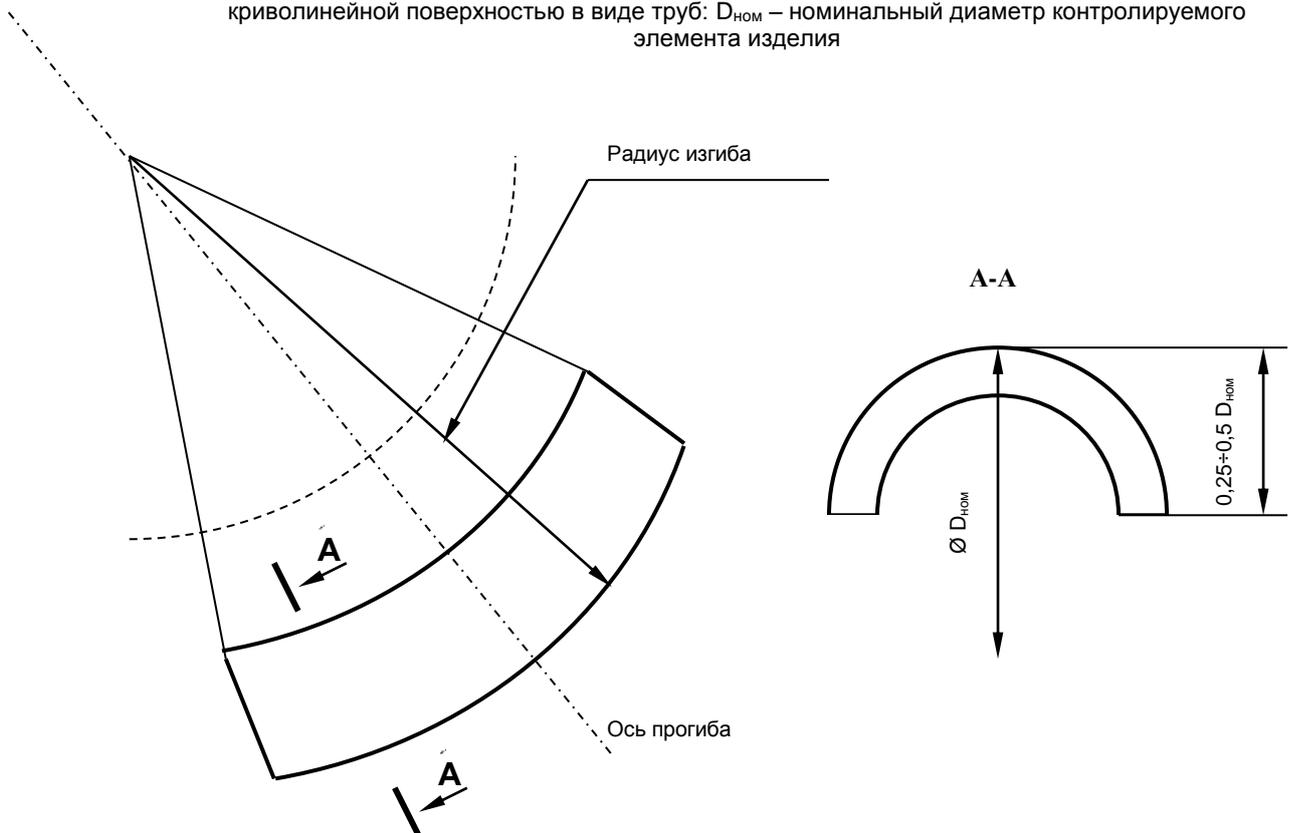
КО для настройки толщиномера при измерении толщины основного металла изделий с криволинейной поверхностью в виде гибов труб: $D_{НОМ}$ – номинальный диаметр контролируемого элемента изделия
